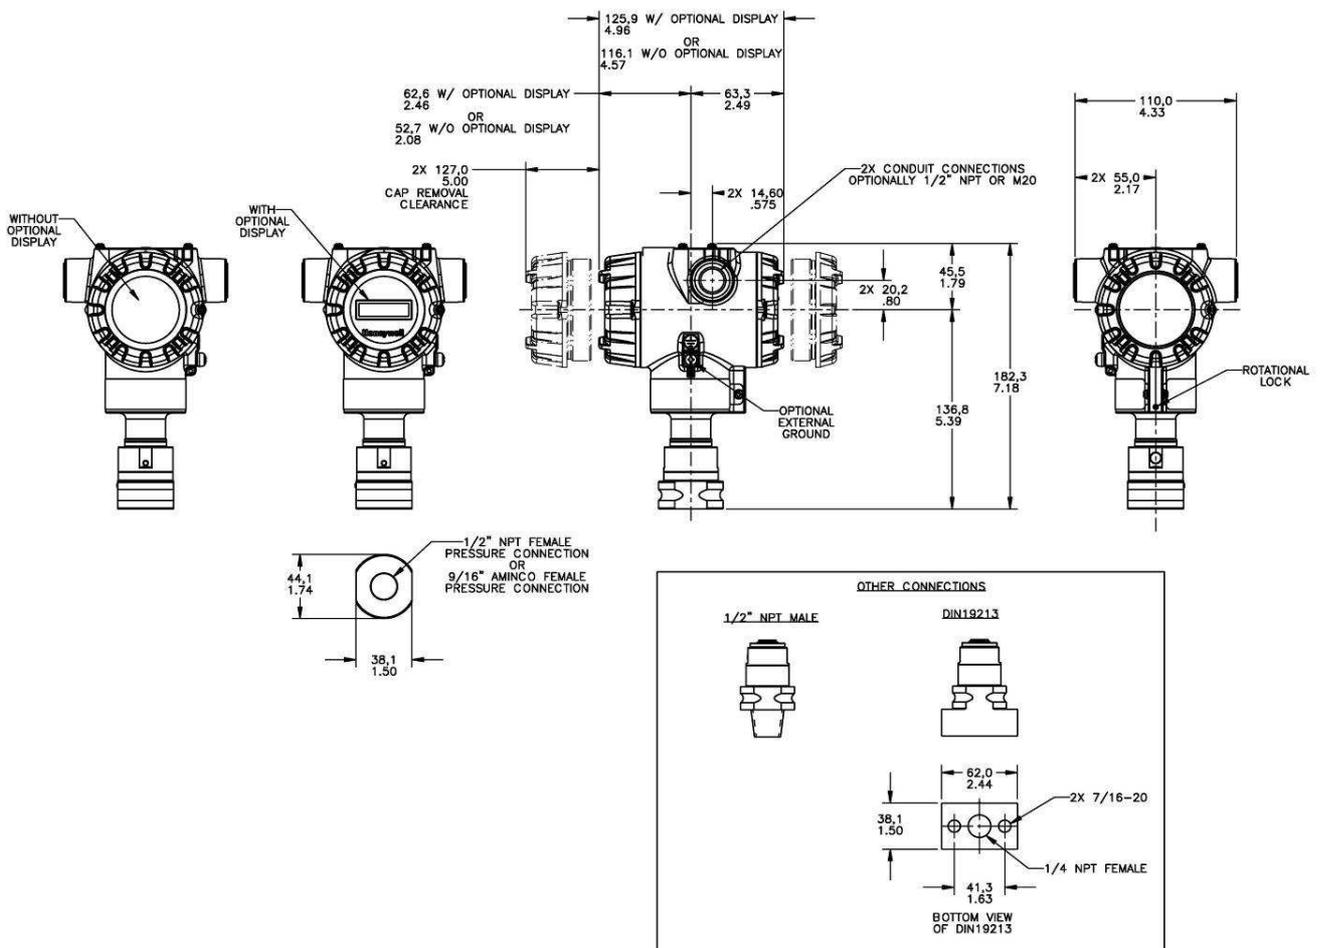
Dimensiuni tipice de montaj pentru STA72L, STA74L si STA77L drept referinta
